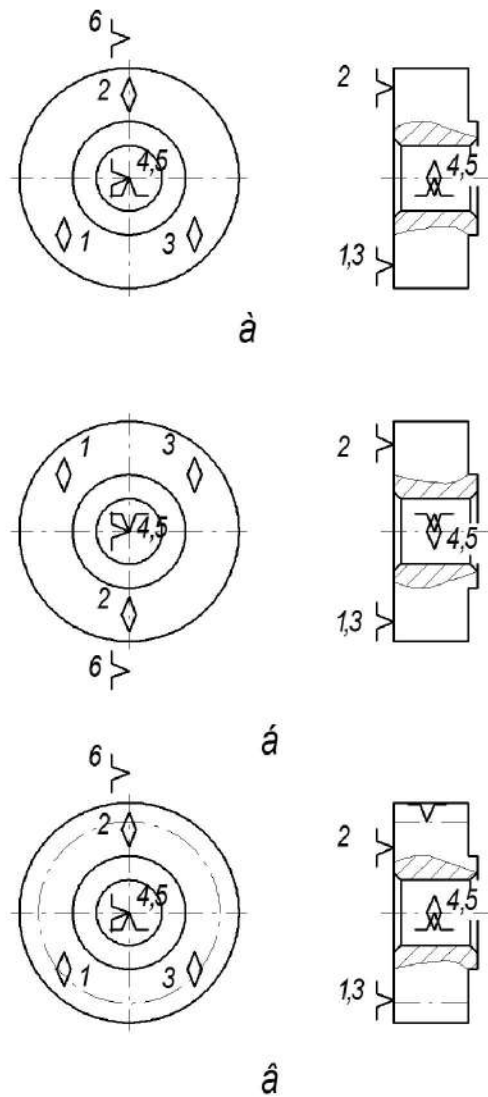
Схеми базування заготовки зубчастого колеса для операцій оброблення: *a* – для токарної операції; *б* – для протяжної операції; *в* – для шліфувальної операції
